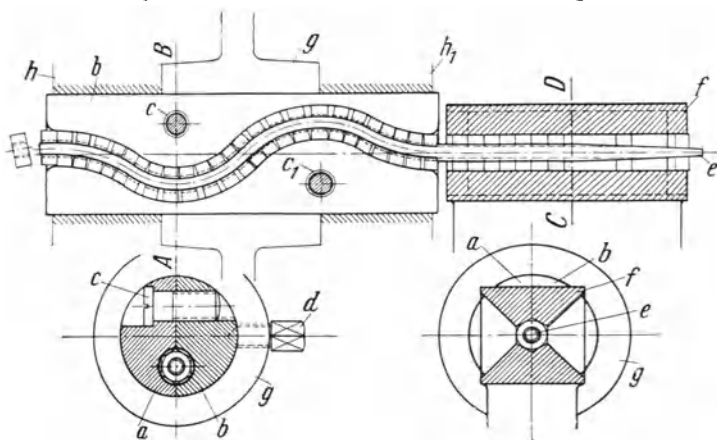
Sondervorrichtung zum Gewindeschneiden kleiner Bronze- oder Messingmuttern.
